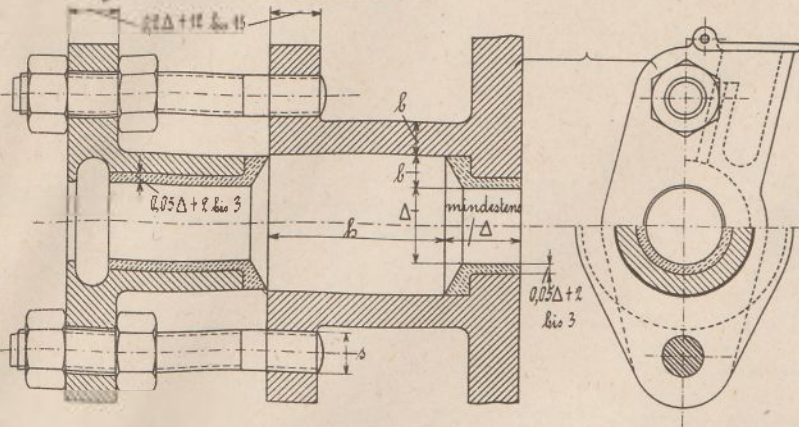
$\frac{1}{5}$ . 1 Brillenschraube.
